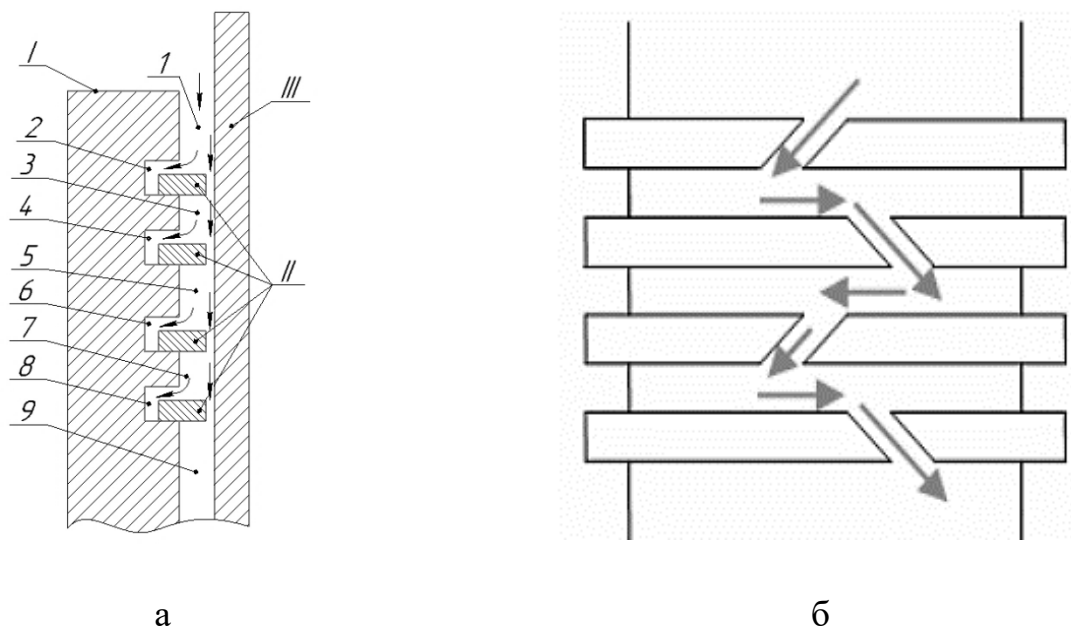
Схема розташування зазорів: а – шляхи витоку газу; б – I – поршень, II – кільця, III – гільза циліндра; 1...9 – зазори
